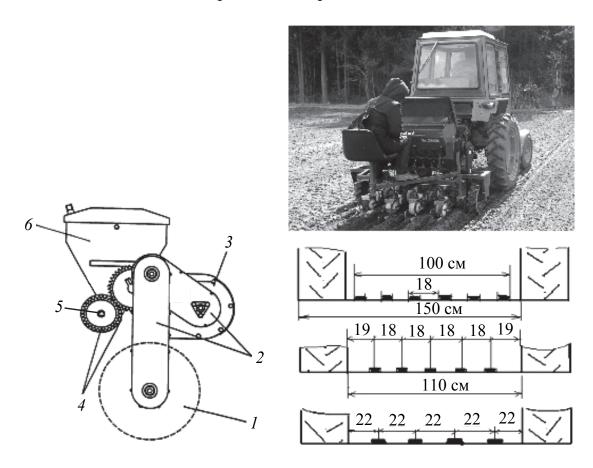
Основные узлы сеялки «Эгедаль»: 1 — приводное колесо; 2 — цепные передачи; 3 — многоступенчатый редуктор; 4 — двухступенчатая зубчатая передача; 5 — вал высевающих аппаратов; 6 — бункер
